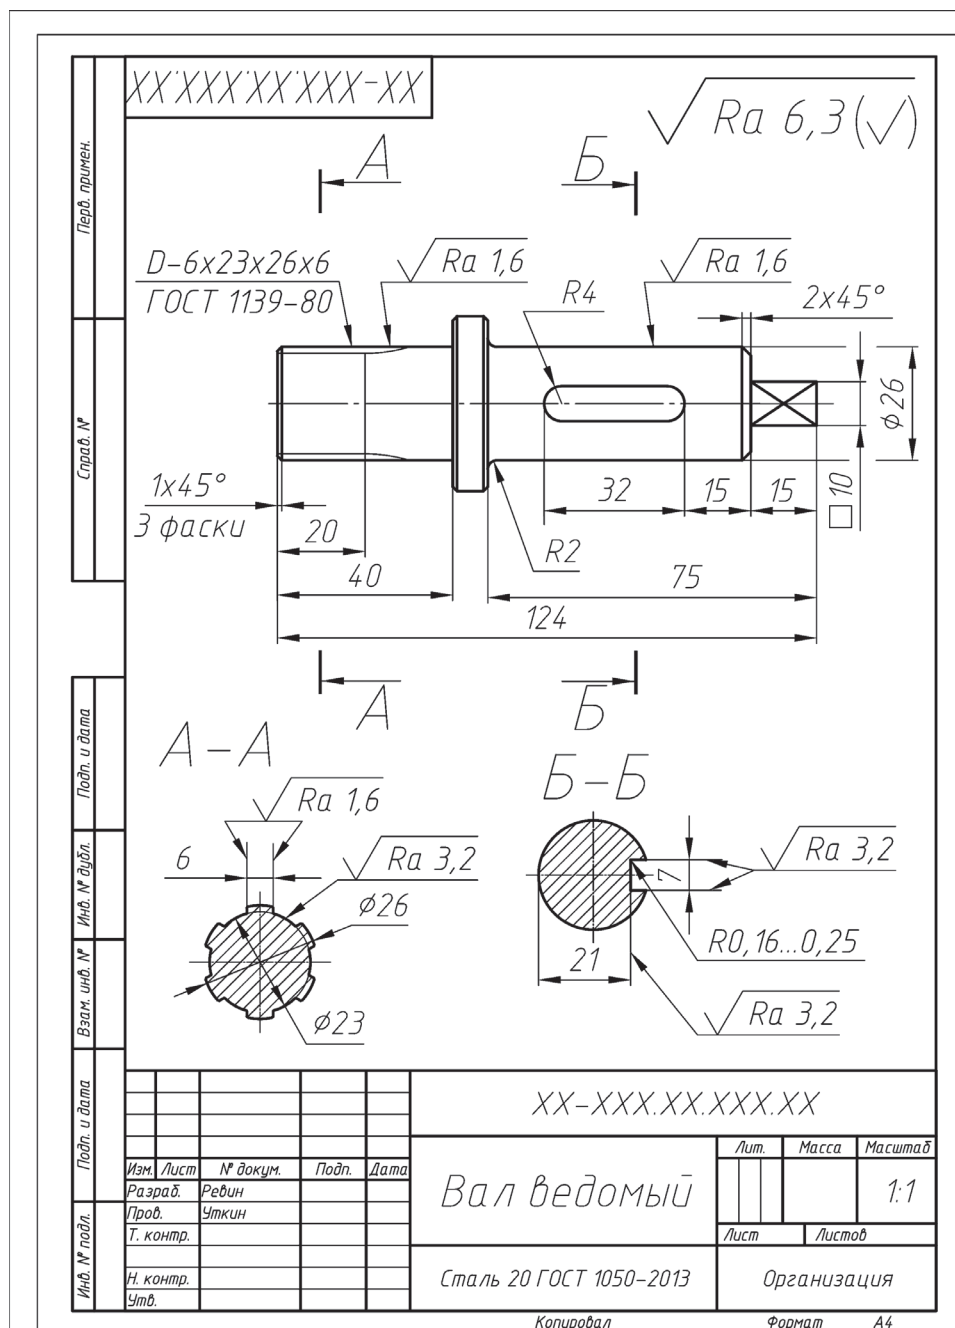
Пример выполнения чертежа детали «Вал» с прямобочным шлицевым участком, призматическим шпоночным пазом и призматическим торцевым участком
